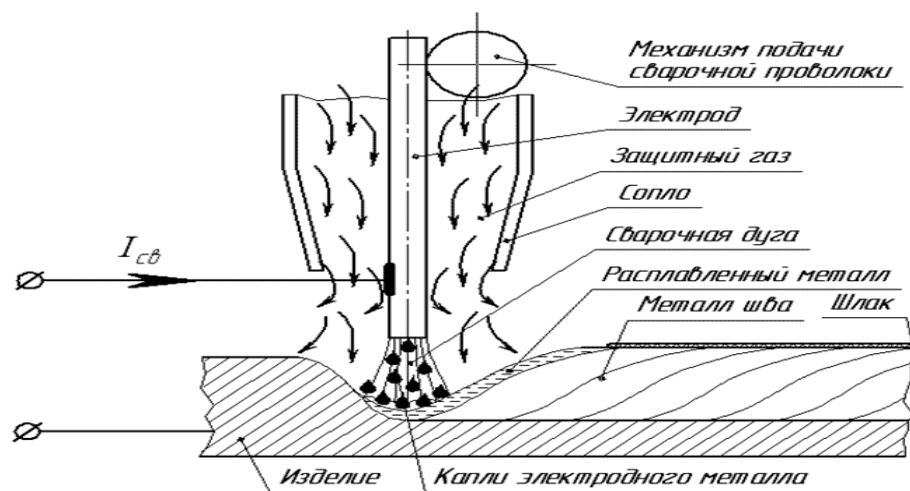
Схема сварки плавящимся электродом в среде защитных газов
